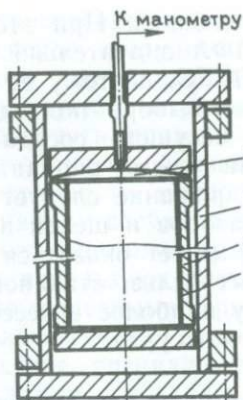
Плавающая футеровка с камерой малого объема для контроля давления:
